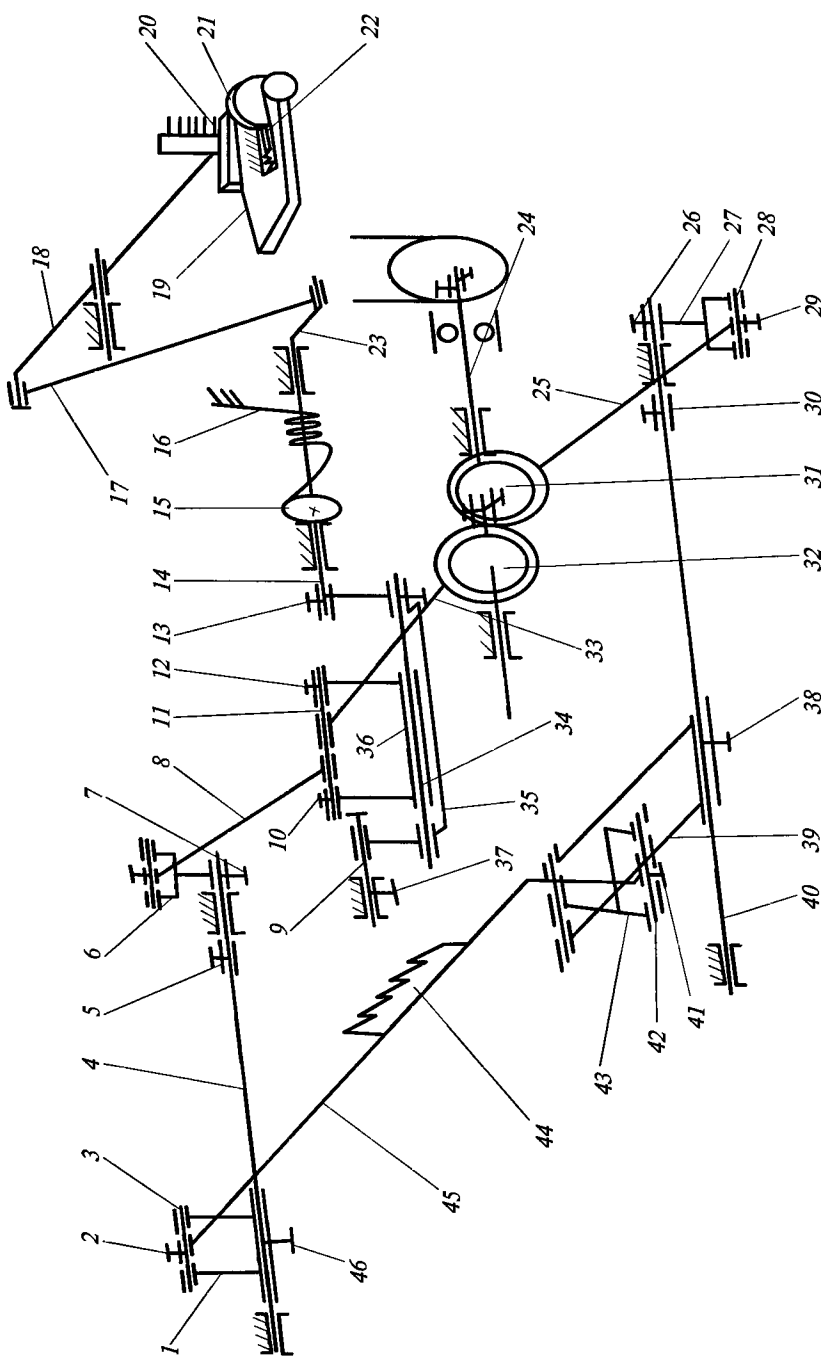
Кинематическая схема механизма перемещения рейки в швейной машине класса 1022М
